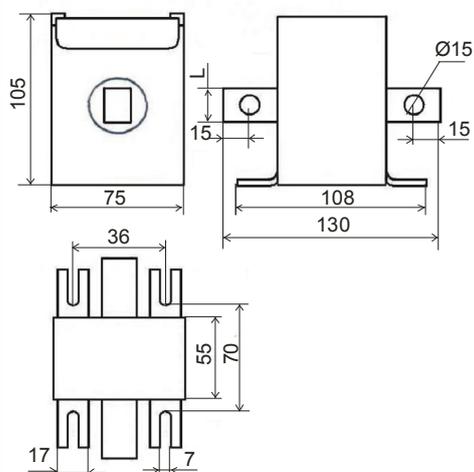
Габаритные размеры трансформатора Т-0,66
